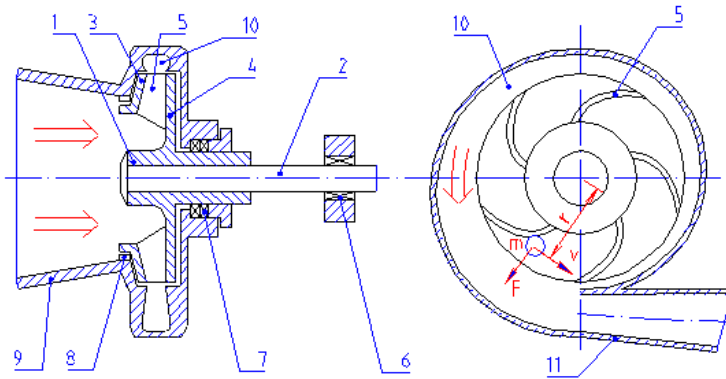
Схема відцентрового насоса: 1 – робоче колесо; 2 – вал; 3 – покривний (передній) диск; 4 – основний (задній) диск; 5 – лопаті; 6 – підшипники; 7, 8 – ущільнення; 9 – підвід; 10 – спіральний відвід; 11 – напірний патрубок
